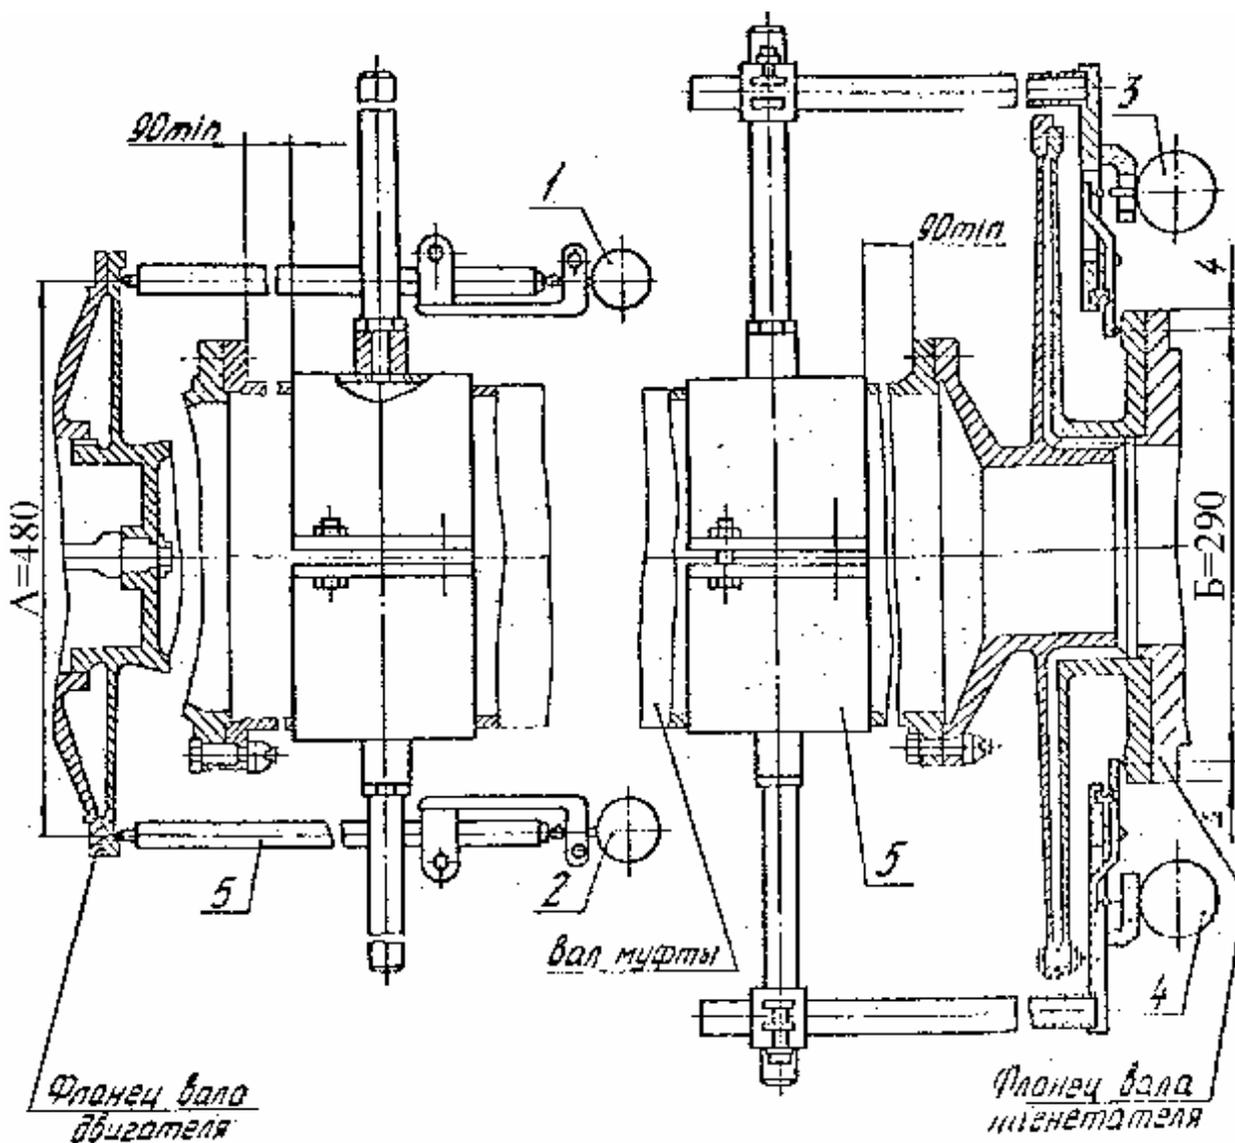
Схема установки приспособлений на валу муфты ГПА-16 «Волга» для контроля перекоса осей
